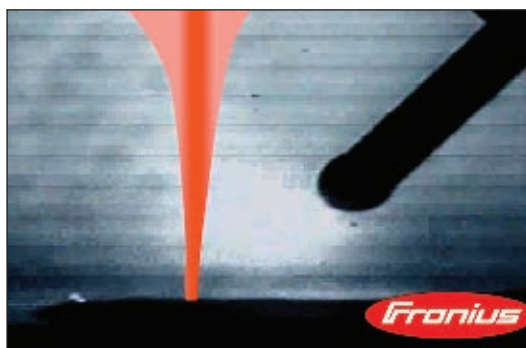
Схематическое представление процесса лазерной GMAW-сварки
